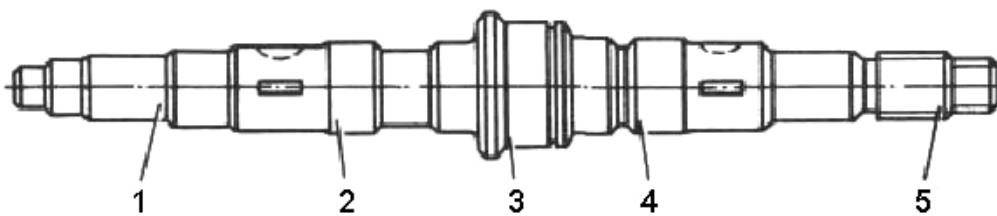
Расположение шеек промежуточного вала раздаточной коробки:
